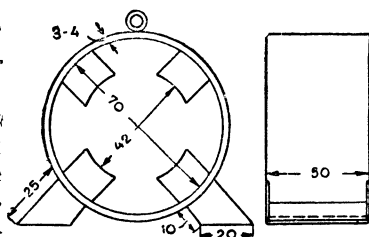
Кольцо статора с башмаками и лапками. Слева — вид спереди; справа — боковой вид.
